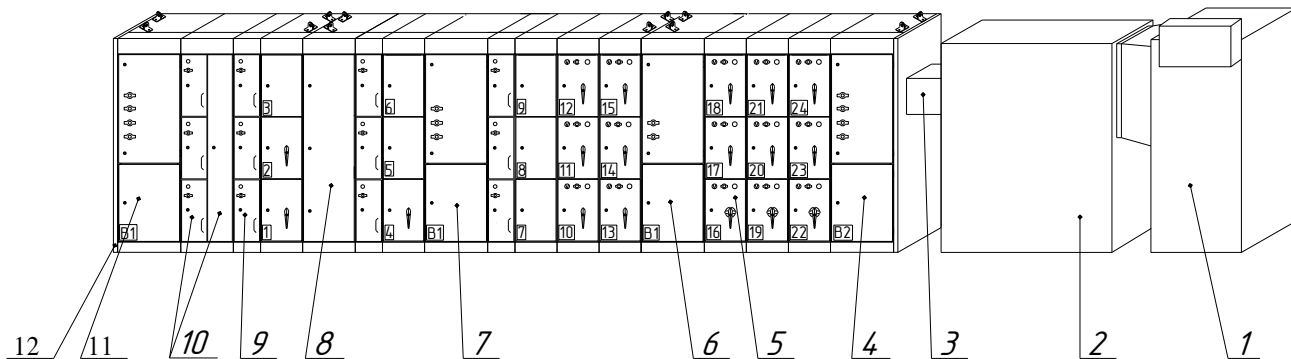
Установка шкафов РУНН на фундамент и ввод кабелей (*- для КТП 1600-3150 кВА)
